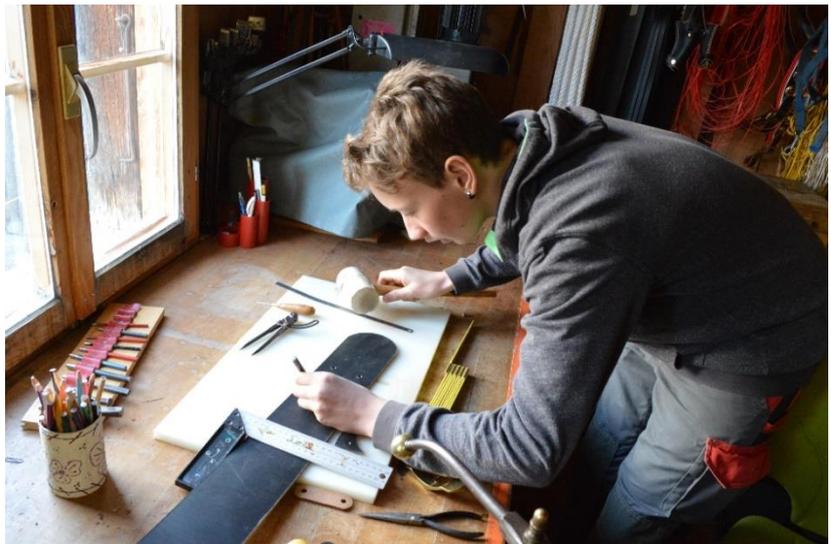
(Bringold, 2019) Hier steche ich die Löcher
